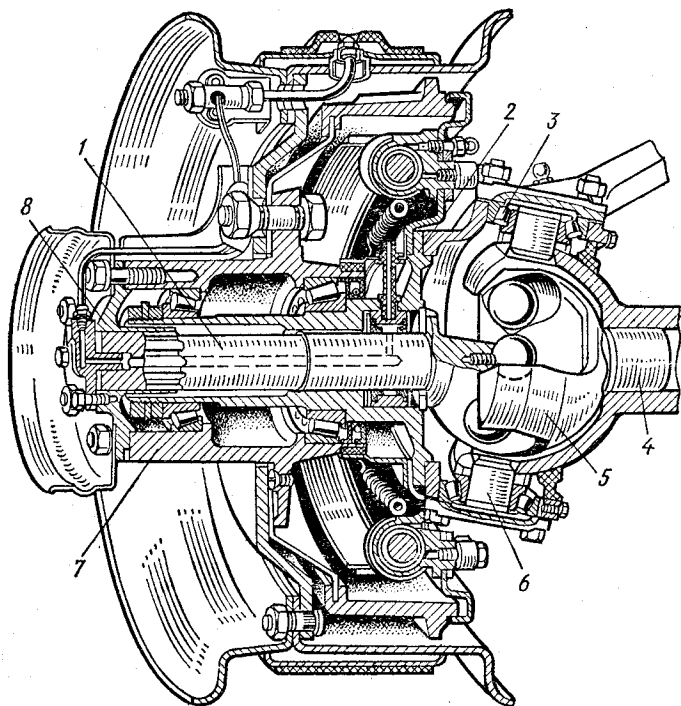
Привод переднього ведучого і керованого колеса }
